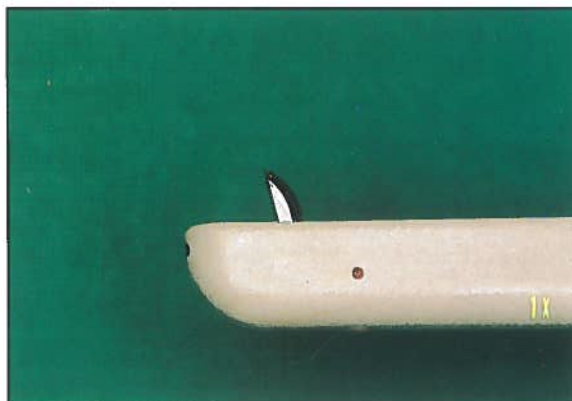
Detalle de la hoja de corte elevada al apretar el gatillo de la pistola.
